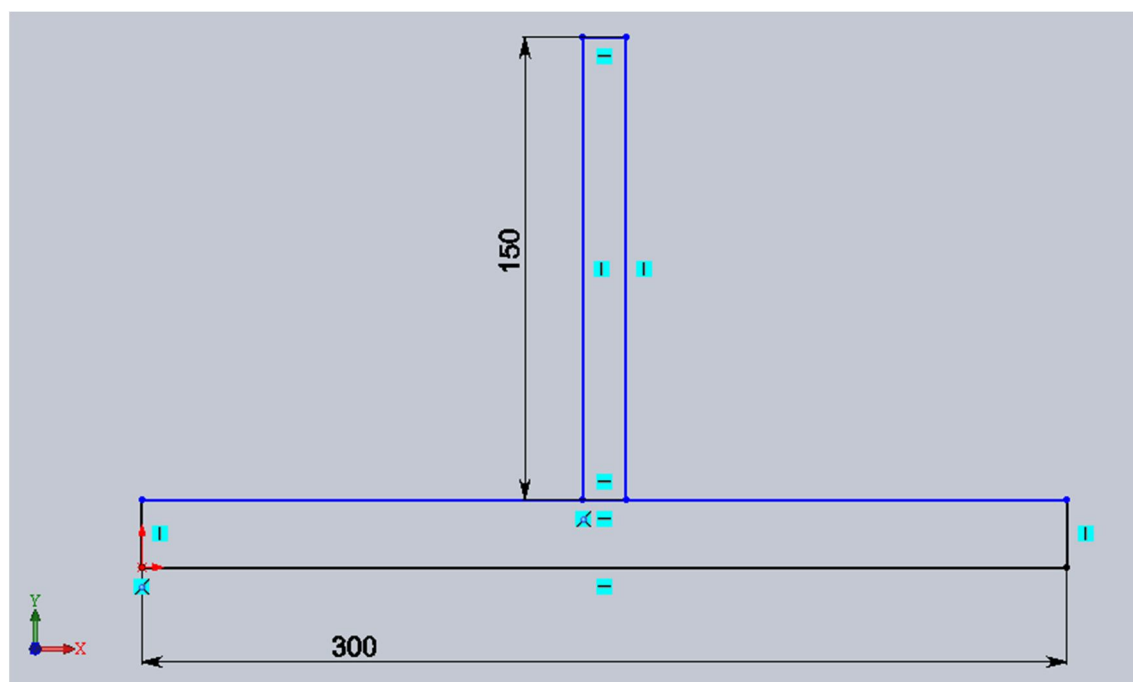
Схема сварного таврового соединения без катетов
